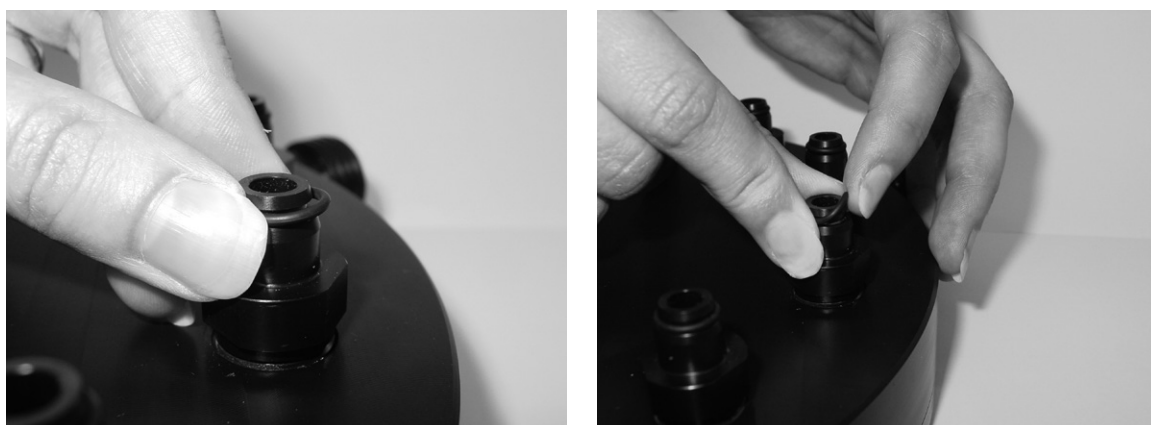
Austauschen der O-Ringe der konischen Adapter
